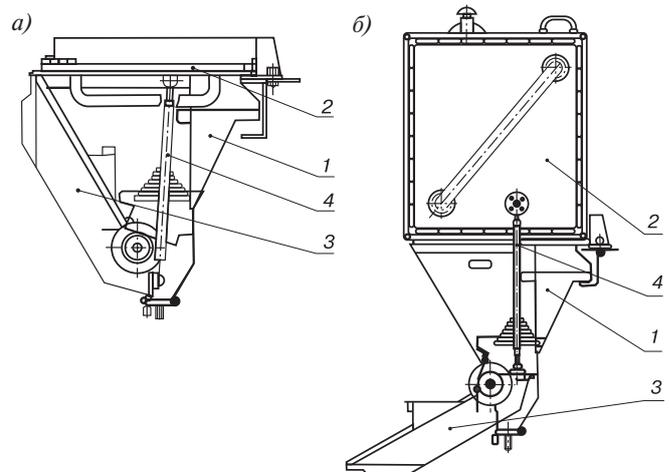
Подножка поворотная закрытая: а — положение «закрыто»; б — положение «открыто»; 1 — корпус; 2 — площадка откидная; 3 — поворотный блок; 4 — толкатель
